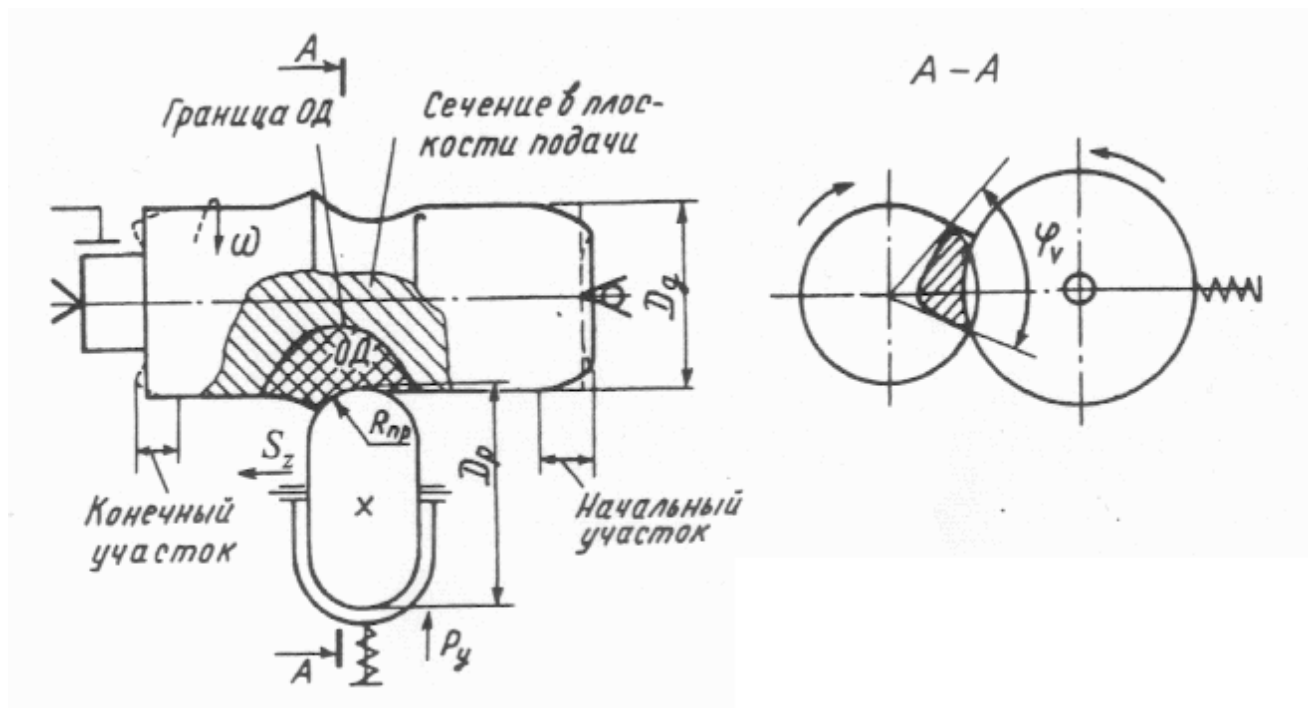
Схема обкатывания вала цилиндрическим роликом
